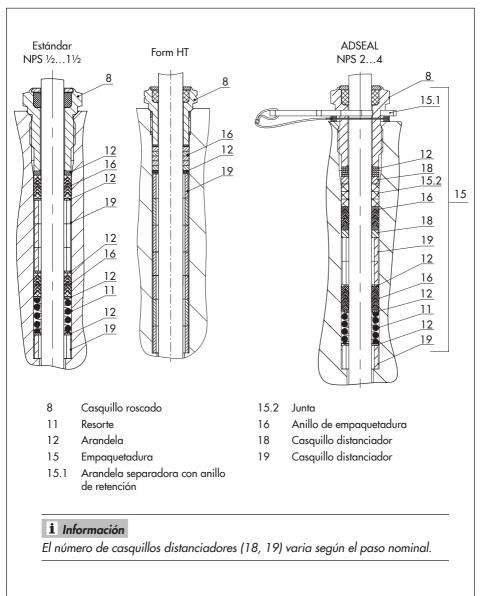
Empaquetaduras: estándar (izquierda) · Form HT (centro) · ADSEAL (derecha)
